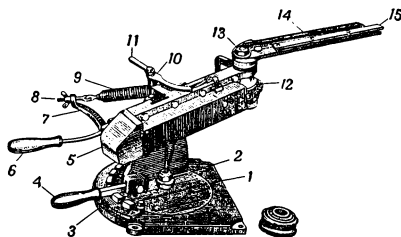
Метательная машинка Ласточкина—Молчанова:
